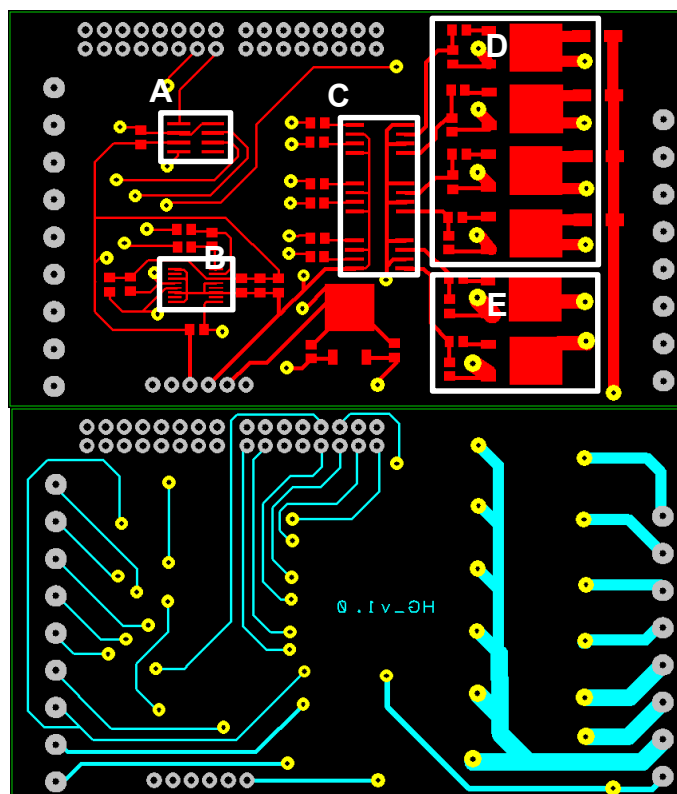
Top layer (cima) e bottom layer (baixo) da PCB do módulo controlo do motor.
